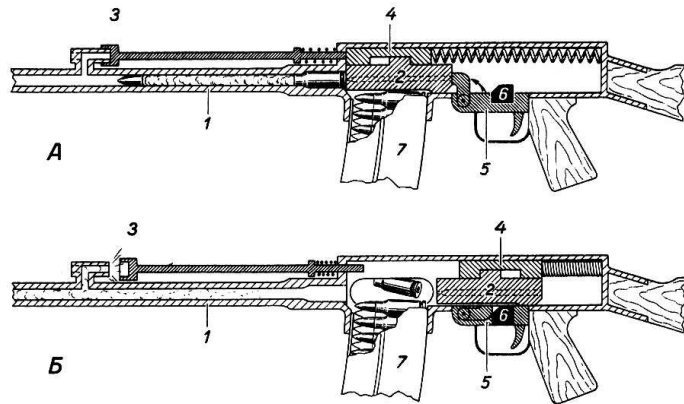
Схема автоматичної зброї з відводом порохових газів із ствола: 1 – ствол; 2 – затвор; 3 – газовідвідний пристрій (газова камера, поршень і шток); 4 – замикаючий пристрій; 5 – ударно-спусковий механізм; 6 – роз'єднувальний пристрій (на зброї безупинного вогню він може відключатися або взагалі бути відсутнім); 7 – магазин. А – рухомі частини в передньому положенні. Б – рухомі частини в крайньому задньому положенні.
